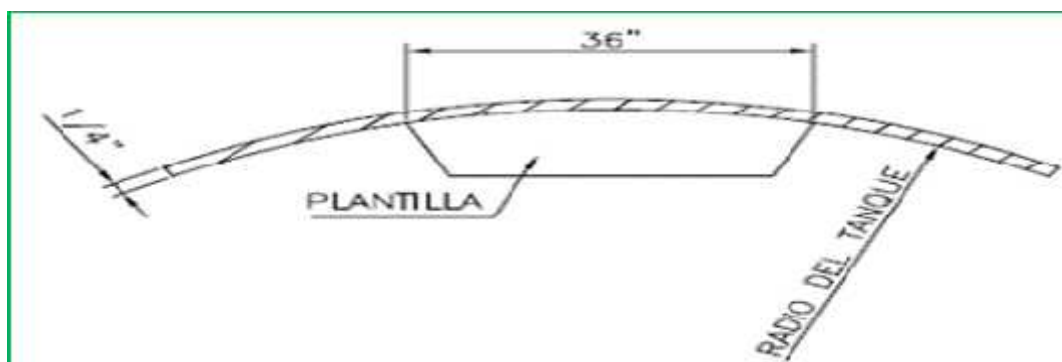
Diagrama de detalle de colocación de plantilla de las planchas ⁷²
